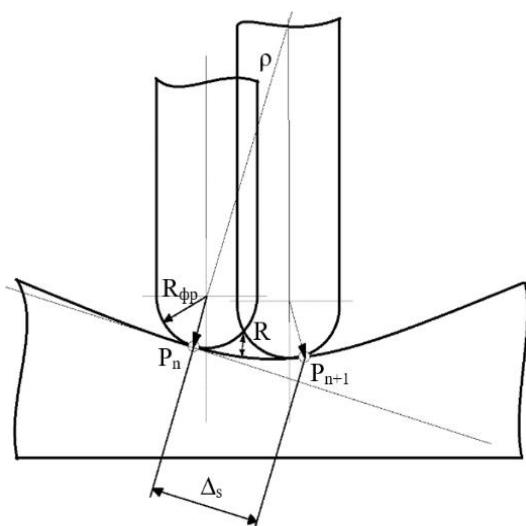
Схема формирования макрорельефа при фрезеровании формообразующей поверхности
